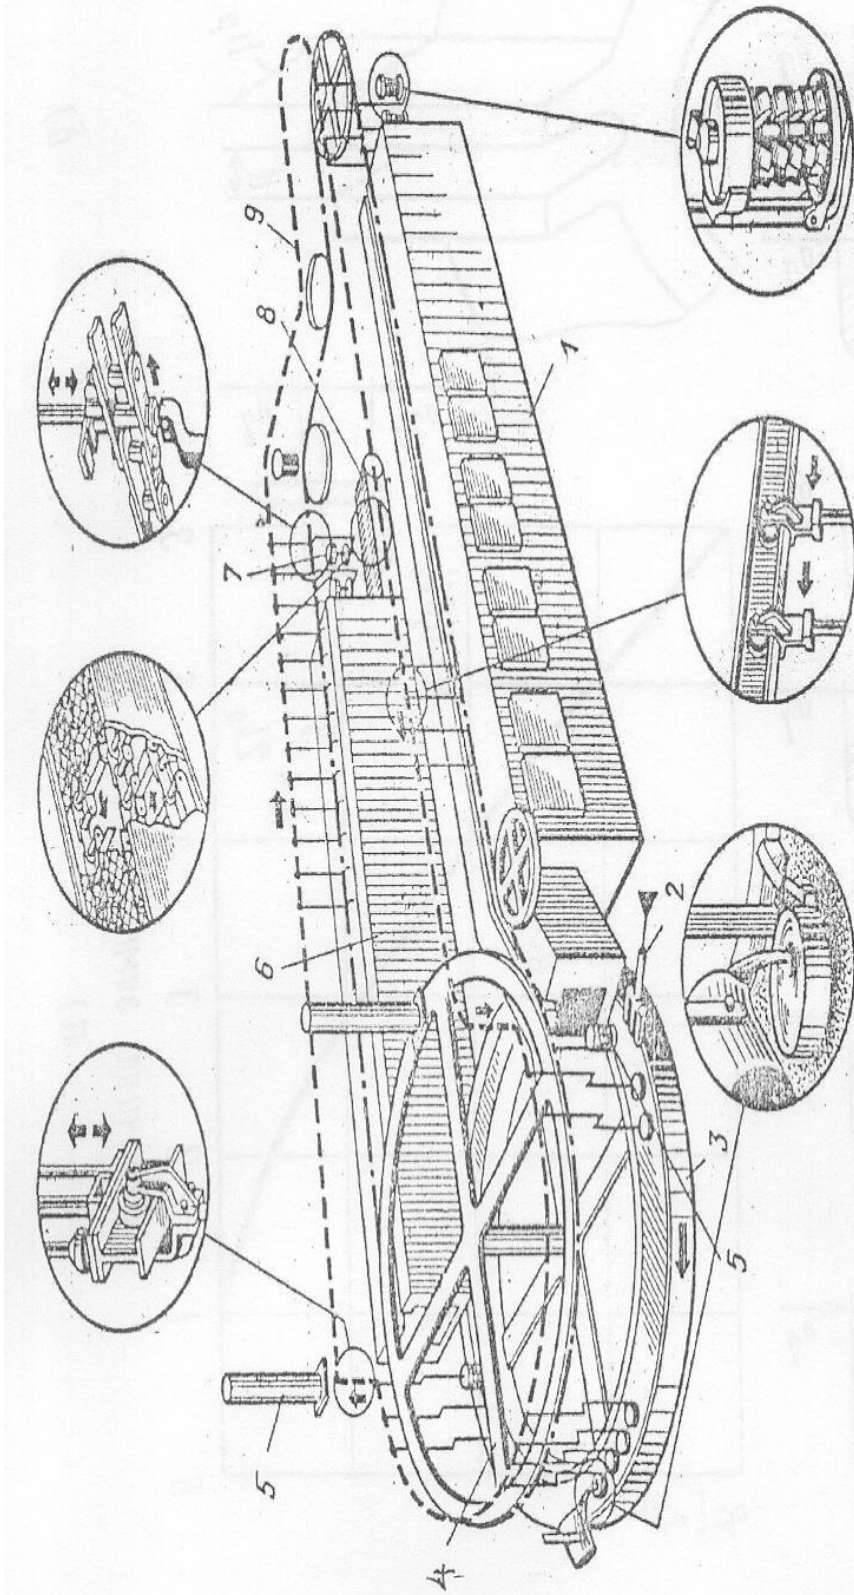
Схема агрегата для прокаливания, формовки, заливки и выбивки оболочковых форм: 1 – газовая печь; 2 – трубы для создания зоны кипящего слоя песка; 3 – заливочная карусель; 4 – звездочка привода цепного конвейера; 5 – пневматические устройства для спуска оболочковых форм в опорный материал в зоне кипящего слоя и извлечения блока затвердевших отливок; 6 – охлаждательная камера; 7 – блок отливок на позиции очистки от остатков керамики; 8 – конвейер для удаления остатков керамики; 9 – конвейер.
